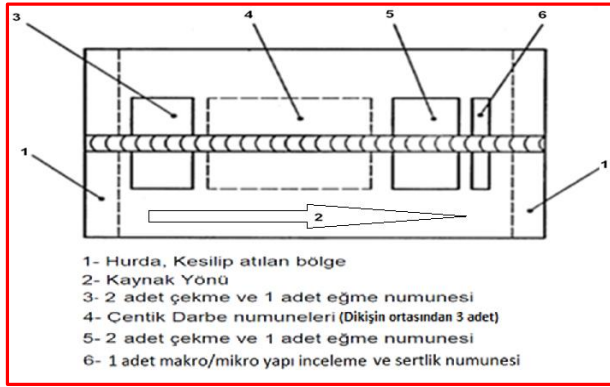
Kaynak işlemi için hazırlanan test parçaları (Test parts prepared for welding process)
